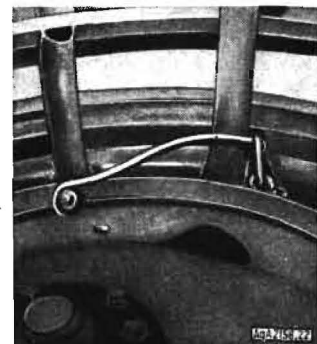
(rechts). Bajonettschnellverschluss mit Spannhebel am Gitterrad
